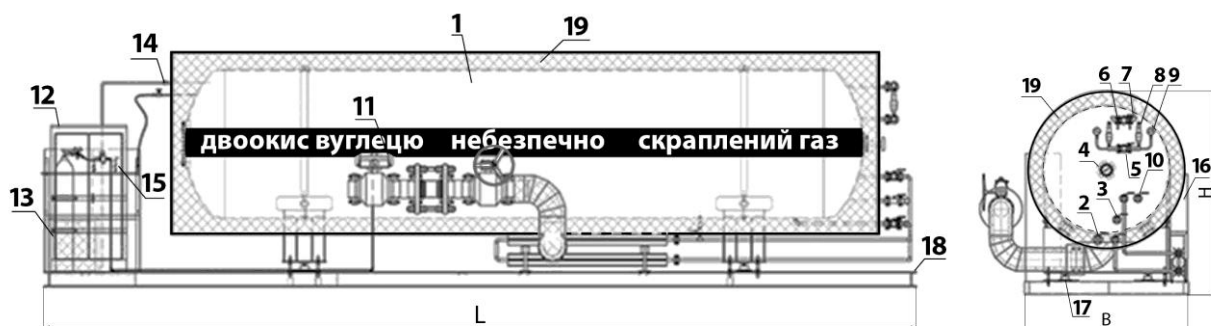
Конструкція резервуара ізотермічного пожежного:
